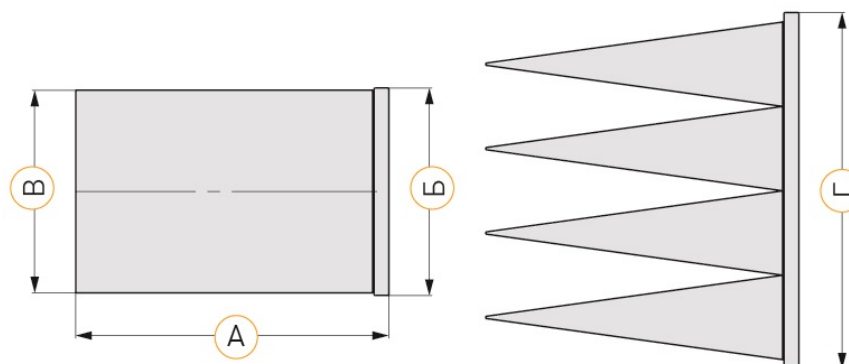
Внешний вид и основные размеры фильтрующих вставок SPU
